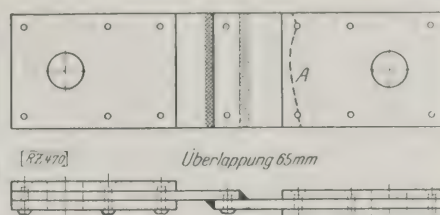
Überlappung mit 19 mm-Nieten, kräftige senkrechte Schweißung.
